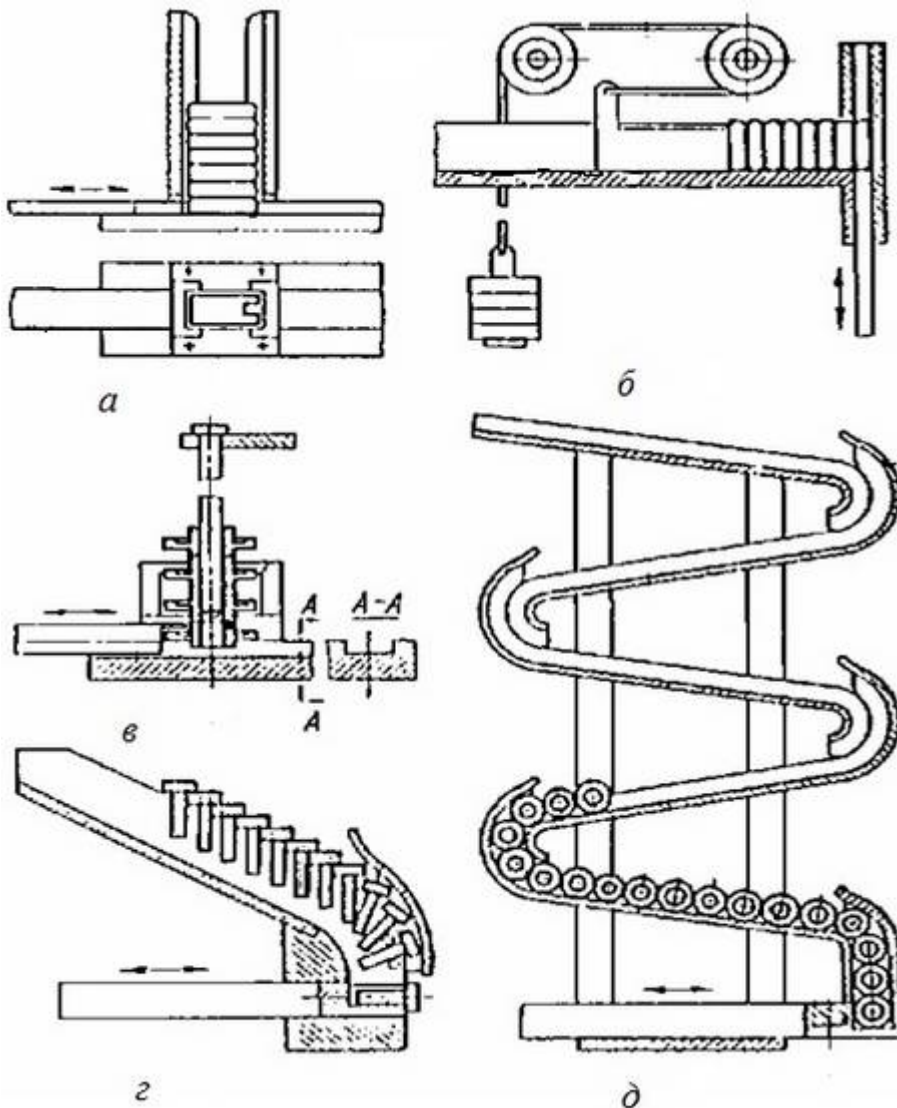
Магазинные загрузочные устройства для заготовок, закладываемых штабелем в один ряд
